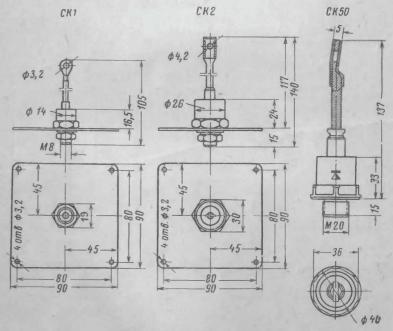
Габаритные чертежи мощных кремниевых стабилитронов и нормированные размеры радиаторов для стабилитронов СК1 и СК2.
